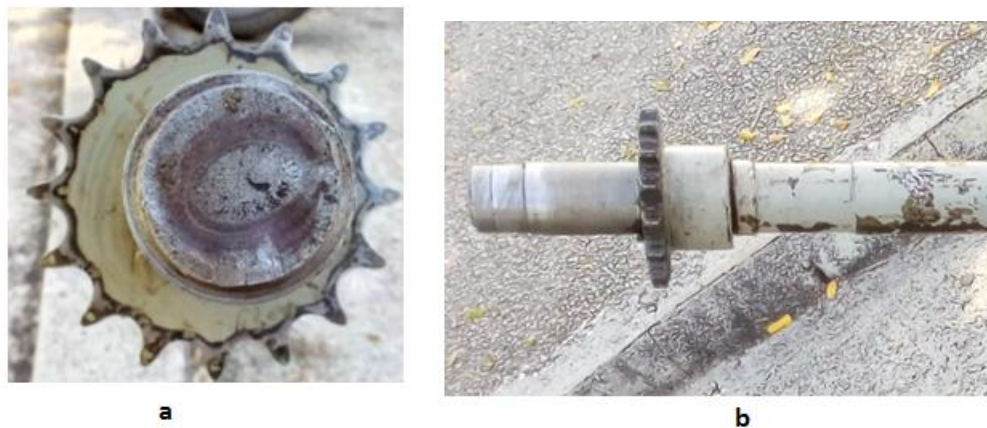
Árbol de transmisión delantero del autocarril TD5M.
